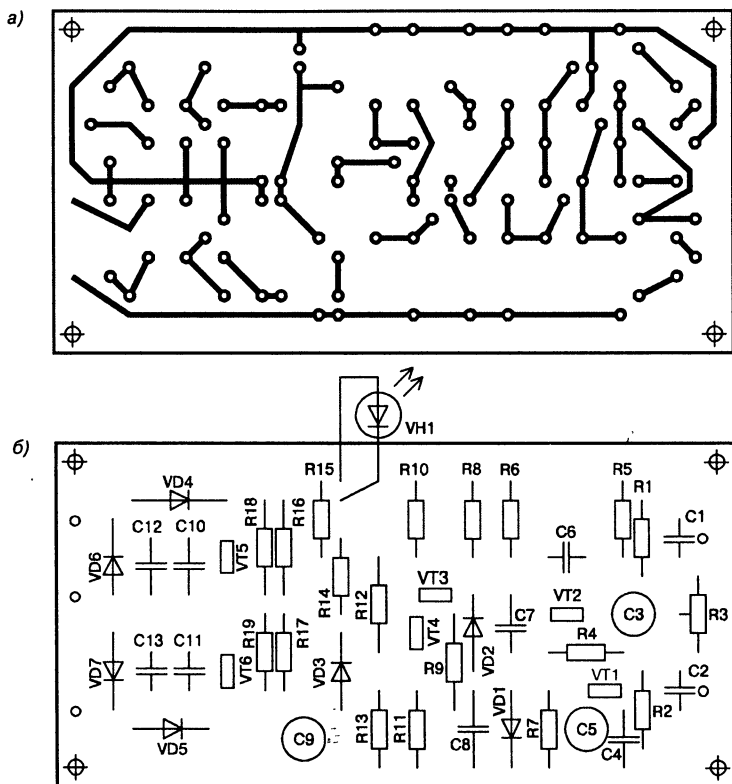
Печатная плата (а) и сборочный чертеж (б) шумоподавителя
